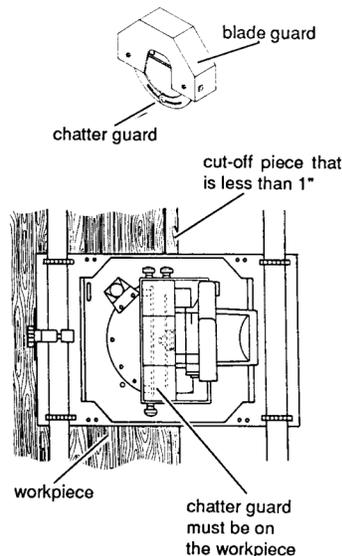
Motor de la Sierra en la posición de corte Horizontal
